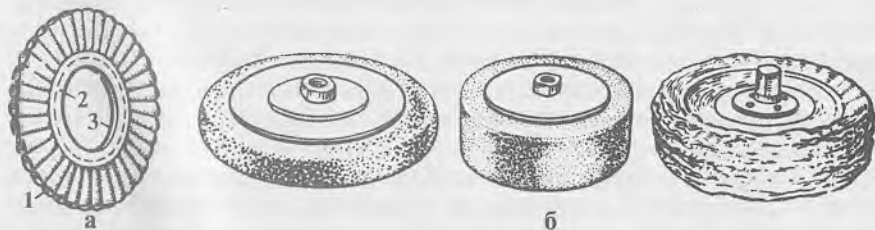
Диски для полирования покрытий на станках (а) и ручными шлифовальными машинами (б):
